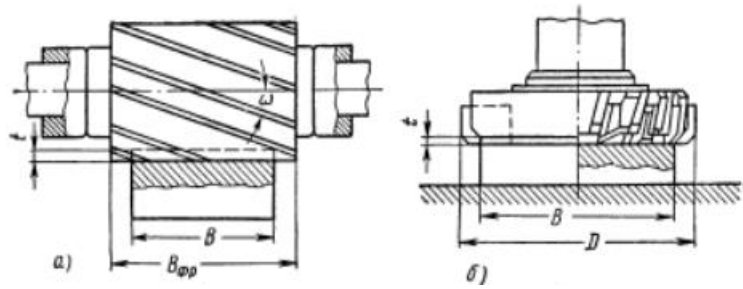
Фрезерування, а)-циліндричною фрезою, б) Торцевою фрезою[3]
